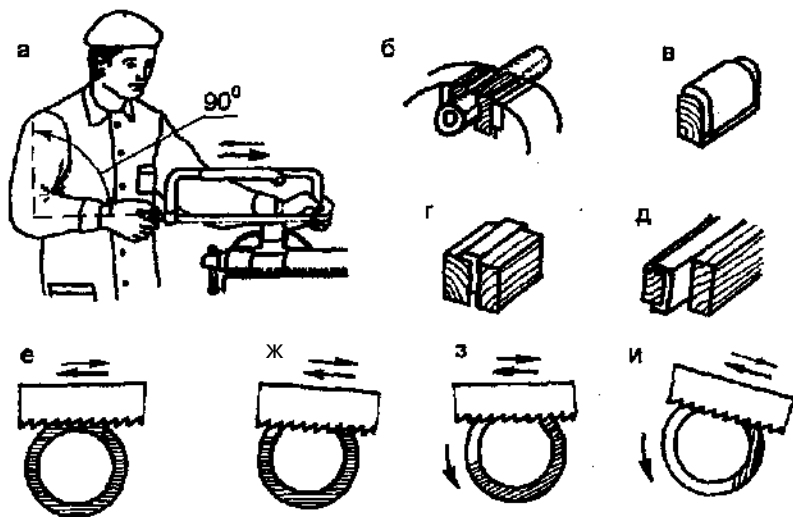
Разрезание ножовкой: а — положение рук и корпуса при работе; б—д — закрепление заготовок в тисках; е—и — последовательность разрезания трубы
